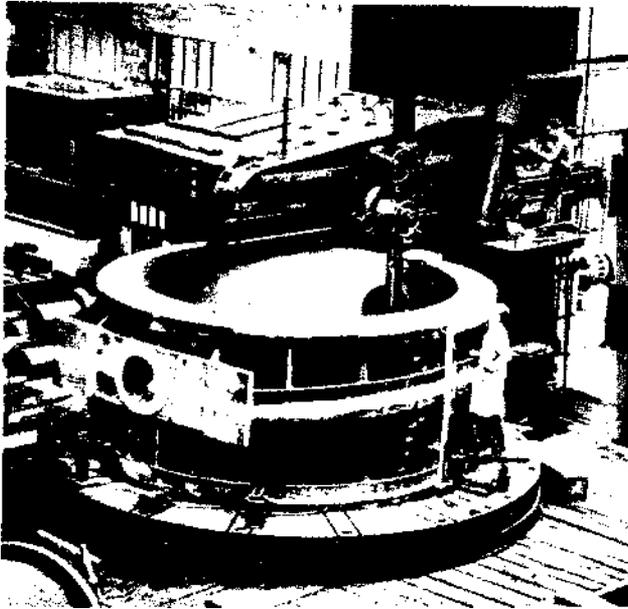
Mandrinado profundo con carro portaherramientas desplazable.
